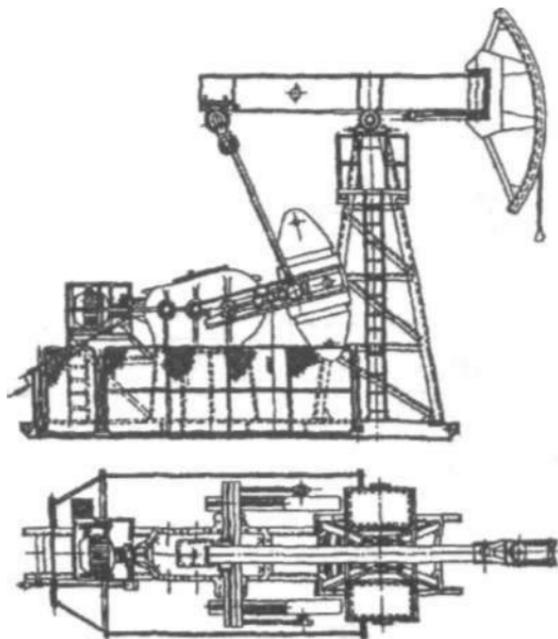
Схема станка - качалки с трехступенчатым коническо-цилиндрическим редуктором
